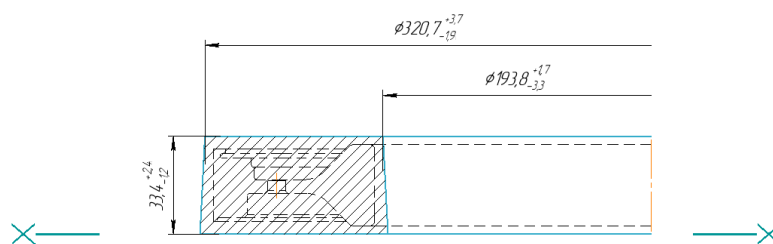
Попередній ескіз заготовки при виготовленні на КГШП
